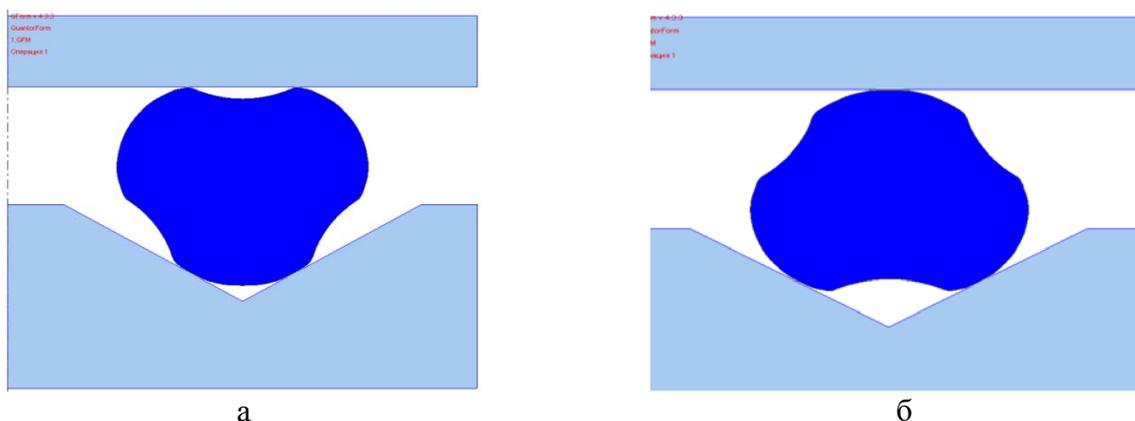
Варианты расположения трёхлучевой заготовки в комбинированных бойках
